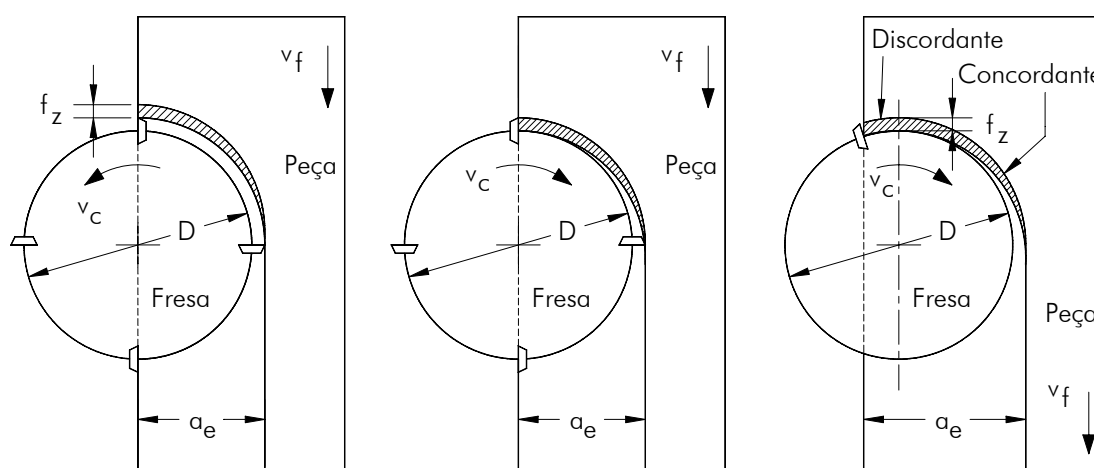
Fresamento frontal: a – Discordante, b – Concordante e c – Simultâneo [11]
